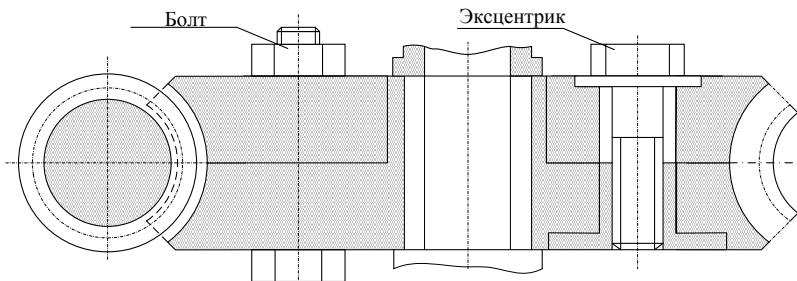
Червячная передача с раздвоенным червячным колесом
